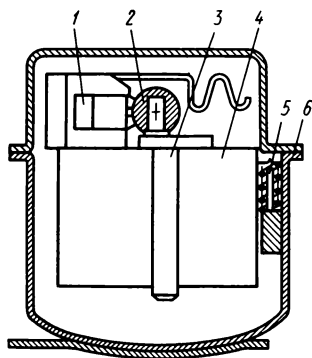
Компрессор ХКВ (ФГ) в сборе
